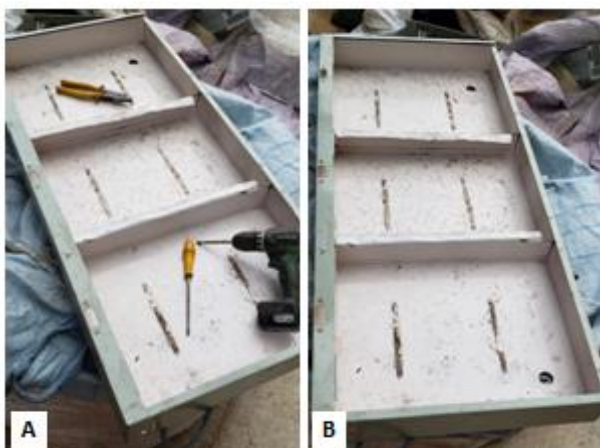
A) Estrutura da caixa do aquecedor em construção; B) Estrutura da caixa do aquecedor finalizada
